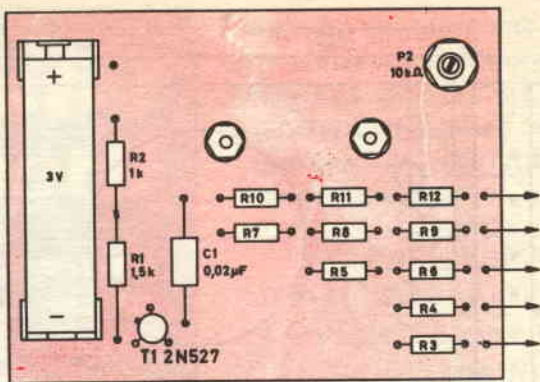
Disposizione dei componenti per il voltmetro elettronico sul circuito stampato visibile nella foto.
